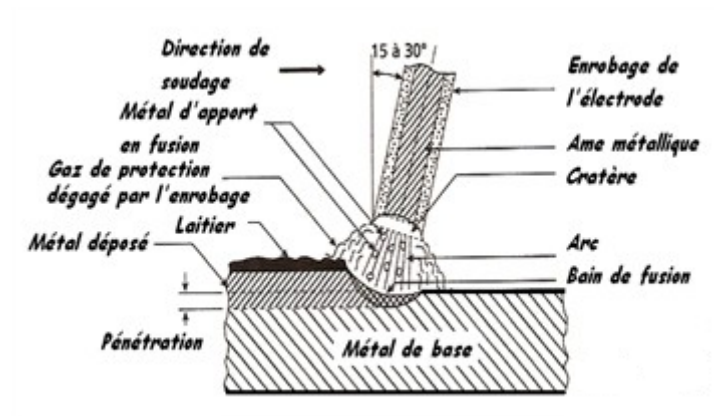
Zone de soudure dans le procédé SAE [52]
